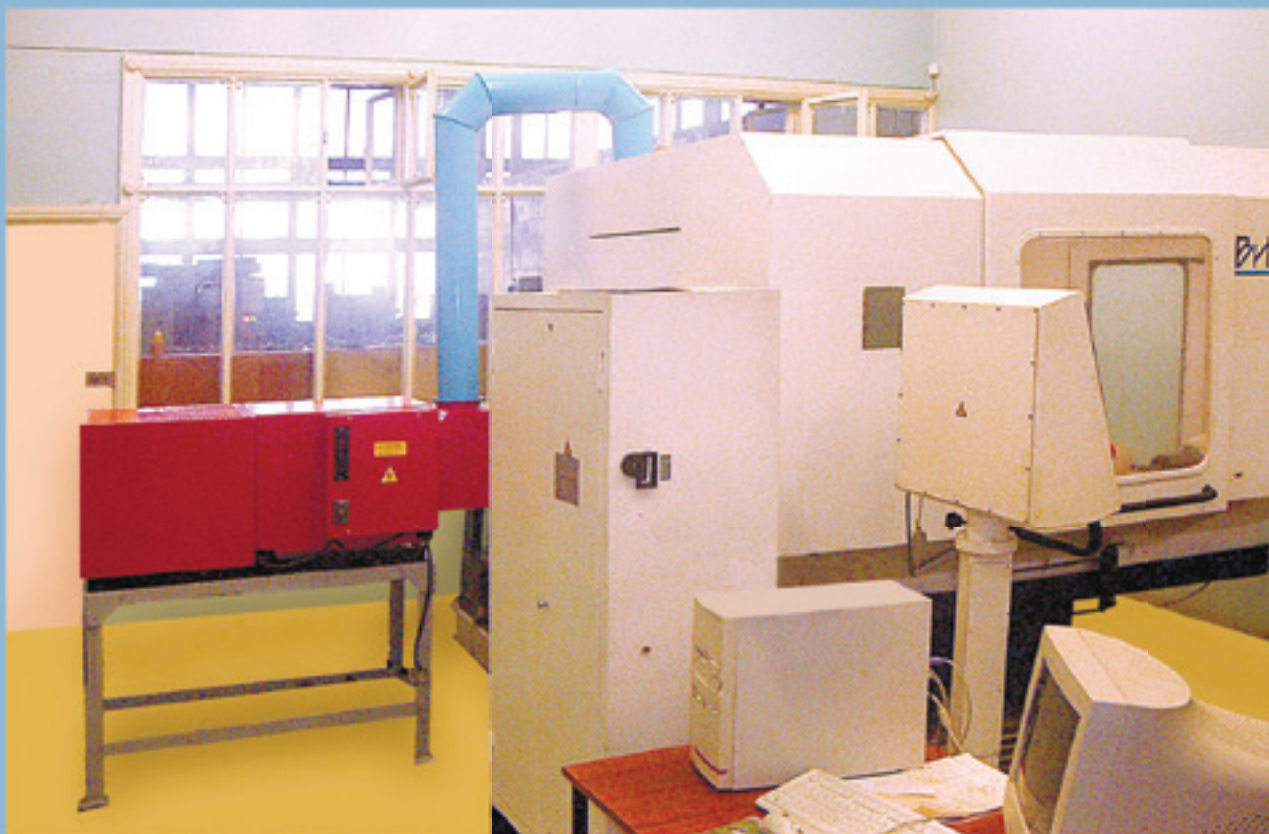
Общий вид, габаритные и присоединительные размеры ЭФВА-МС-40-11М:
